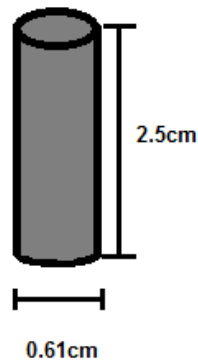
Se muestra las dimensiones del pin utilizado para realizar el ensayo de desgaste.
